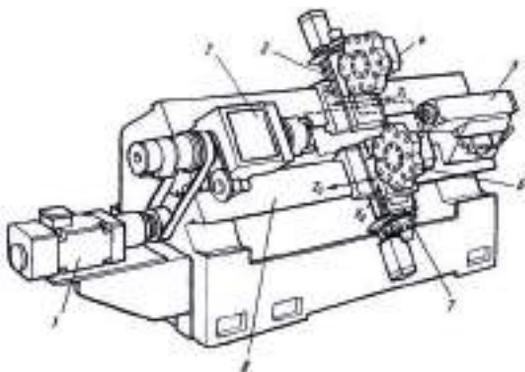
Расположение сдвоенных револьверных головок на токарных станках с ЧПУ
